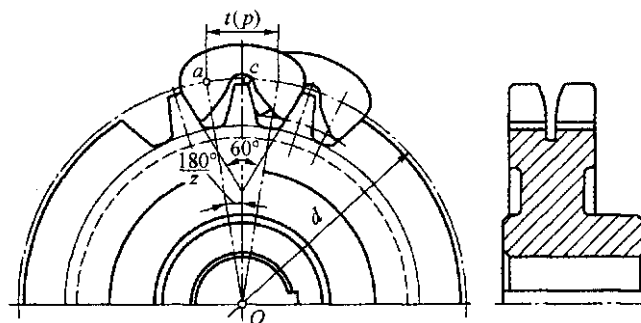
Звездочка зубчатой цепи:
